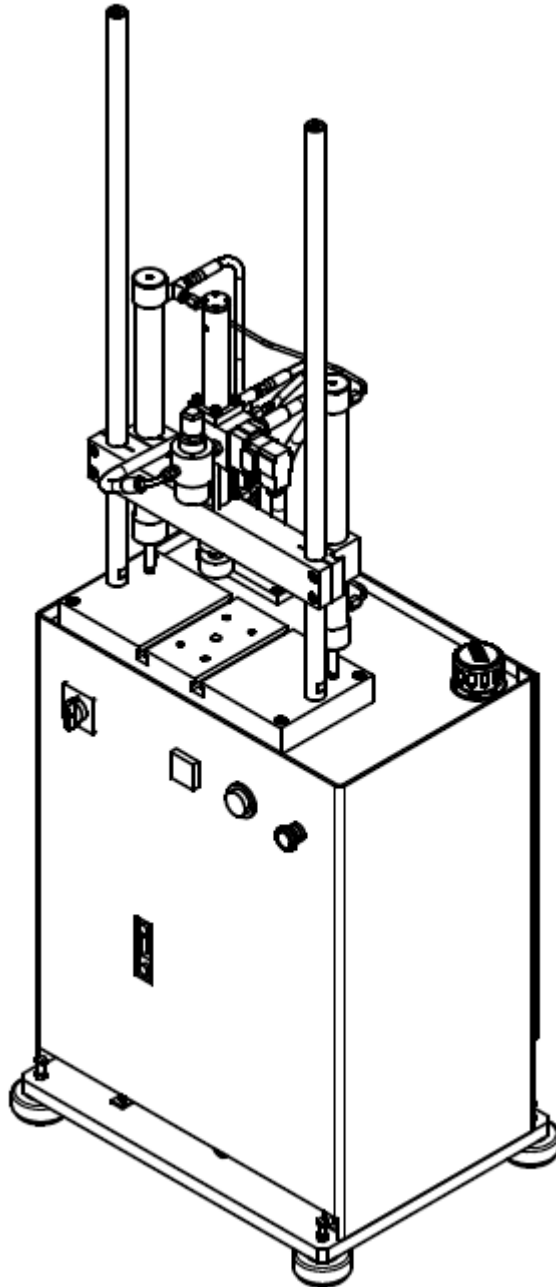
Vista isométrica da montagem da máquina de 500 kg
